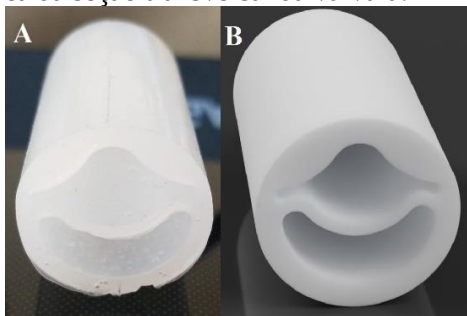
Seção transversal da válvula real (A) projetado (B)
